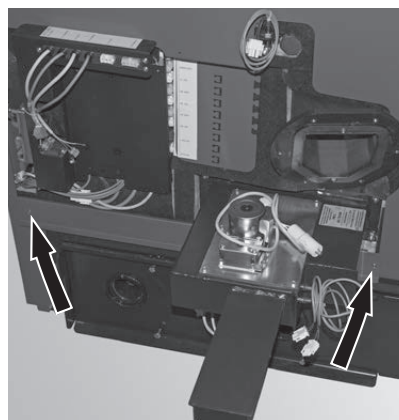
Verkleidung links unten mit 2 Stk. Blechschrauben befestigen
